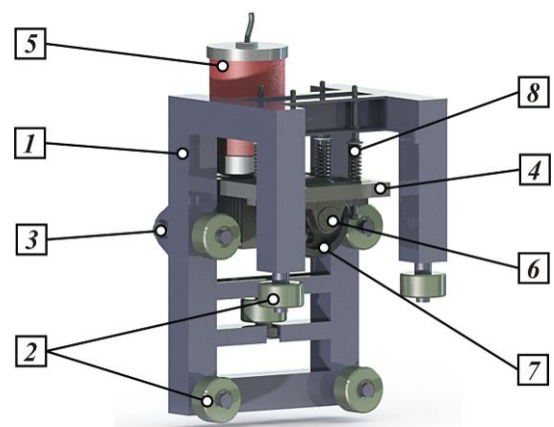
Приводная подвеска: 1, 4 – металлоконструкции несущей и прижимной секции; 2, 7 – холостые и приводной ролики; 3 – ось; 5 – мотор-редуктор; 6 – подшипниковые опоры; 8 – прижимное устройство)
